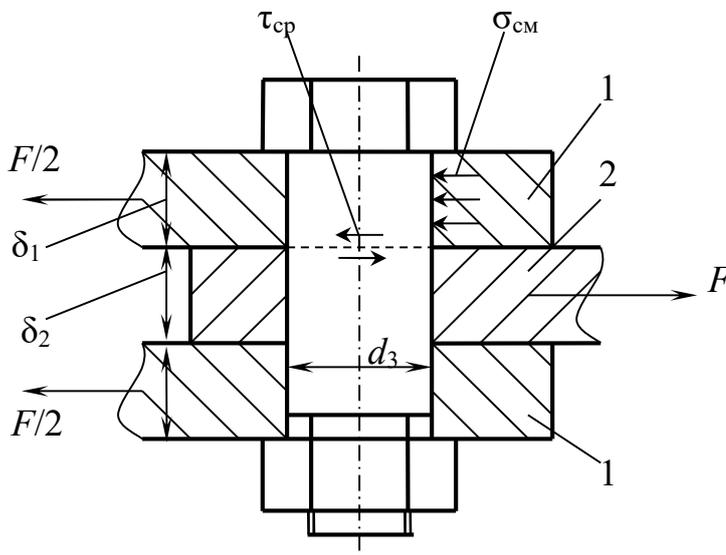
Соединение, нагруженное поперечными силами (болт в отверстии без зазора)
